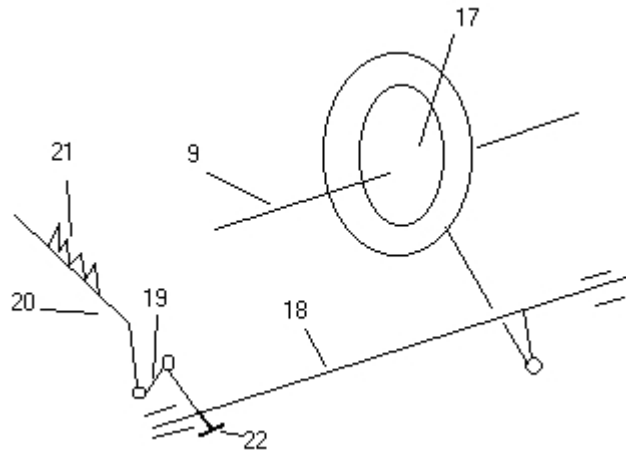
Механізм підйому зубчастої рейки швейної машини 1022М
